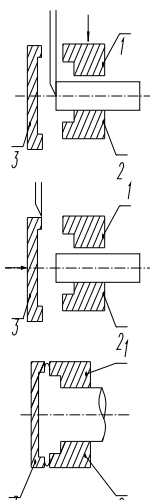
Схема штамповки на горизонтально-ковочной машине
